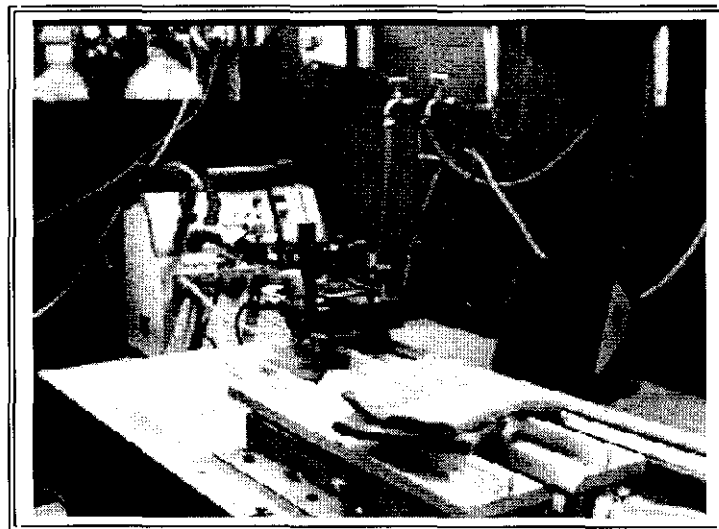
Equipo de soldadura TIG (ARISTOTIG 250 AC/DC).
